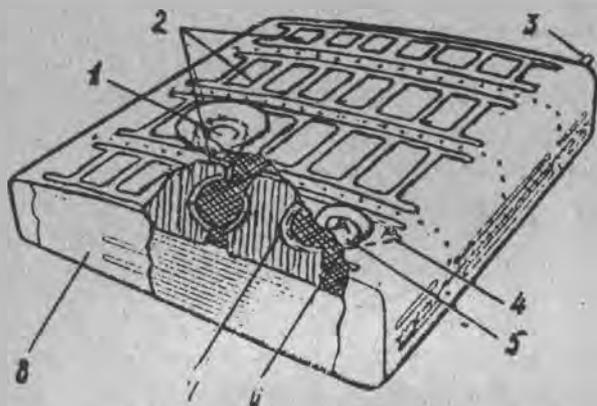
Топливный бак (правой группы): 1 — горловина топливомера; 2 — обечайка, штампованная "карточками"; 3 — соединительный штуцер для заправки от насоса БПК-4; 4 — штуцер дренажа; 5 — заливная горловина; 6 — сетчатый фильтр; 7 — перегородка; 8 — доньшко
